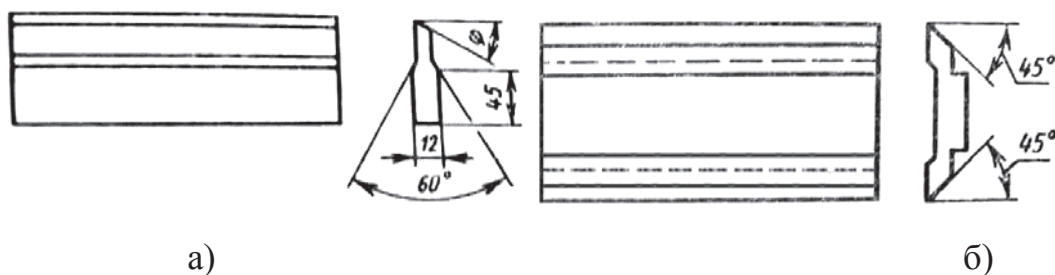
Конструкция и размеры ножа (а), направляющая линейка (б)
